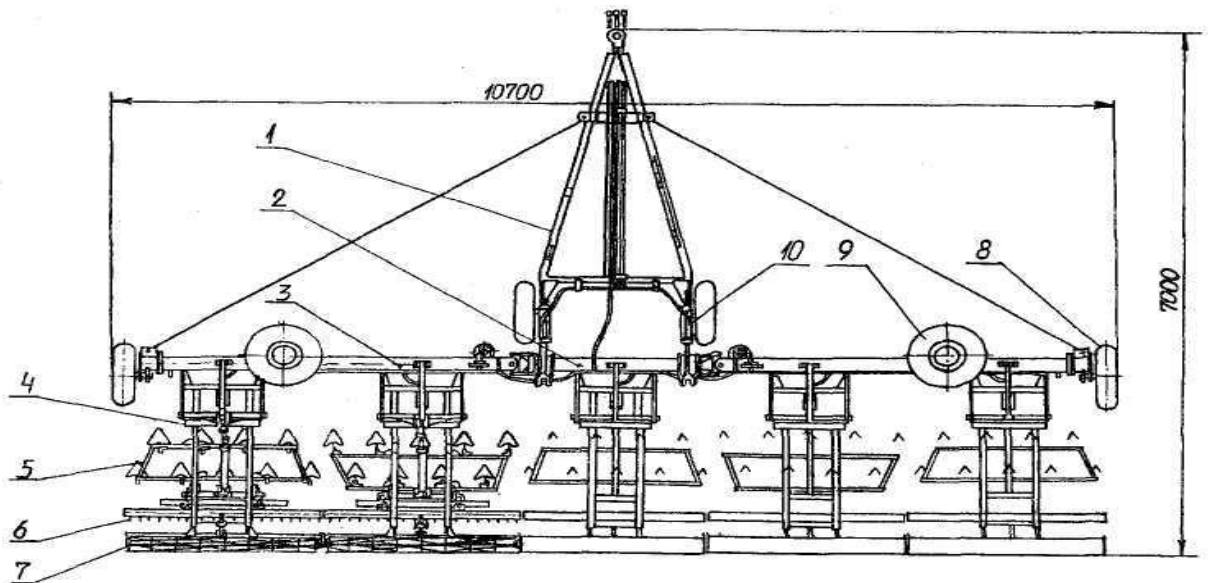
Культиватор блочно-модульный КБМ-10,5П: 1 - сница; 2 - средний блок; 3 - боковой блок; 4 - модули стрелчатых и пружинных рыхлителей; 5 - стрелчатые и пружинные рыхлители; 6 - планочно-зубовой выравниватель; 7 - винтовой прутковый подрессоренный каток; 8 - полевое колесо; 9 - транспортное колесо; 10 - гидроцилиндр управления
